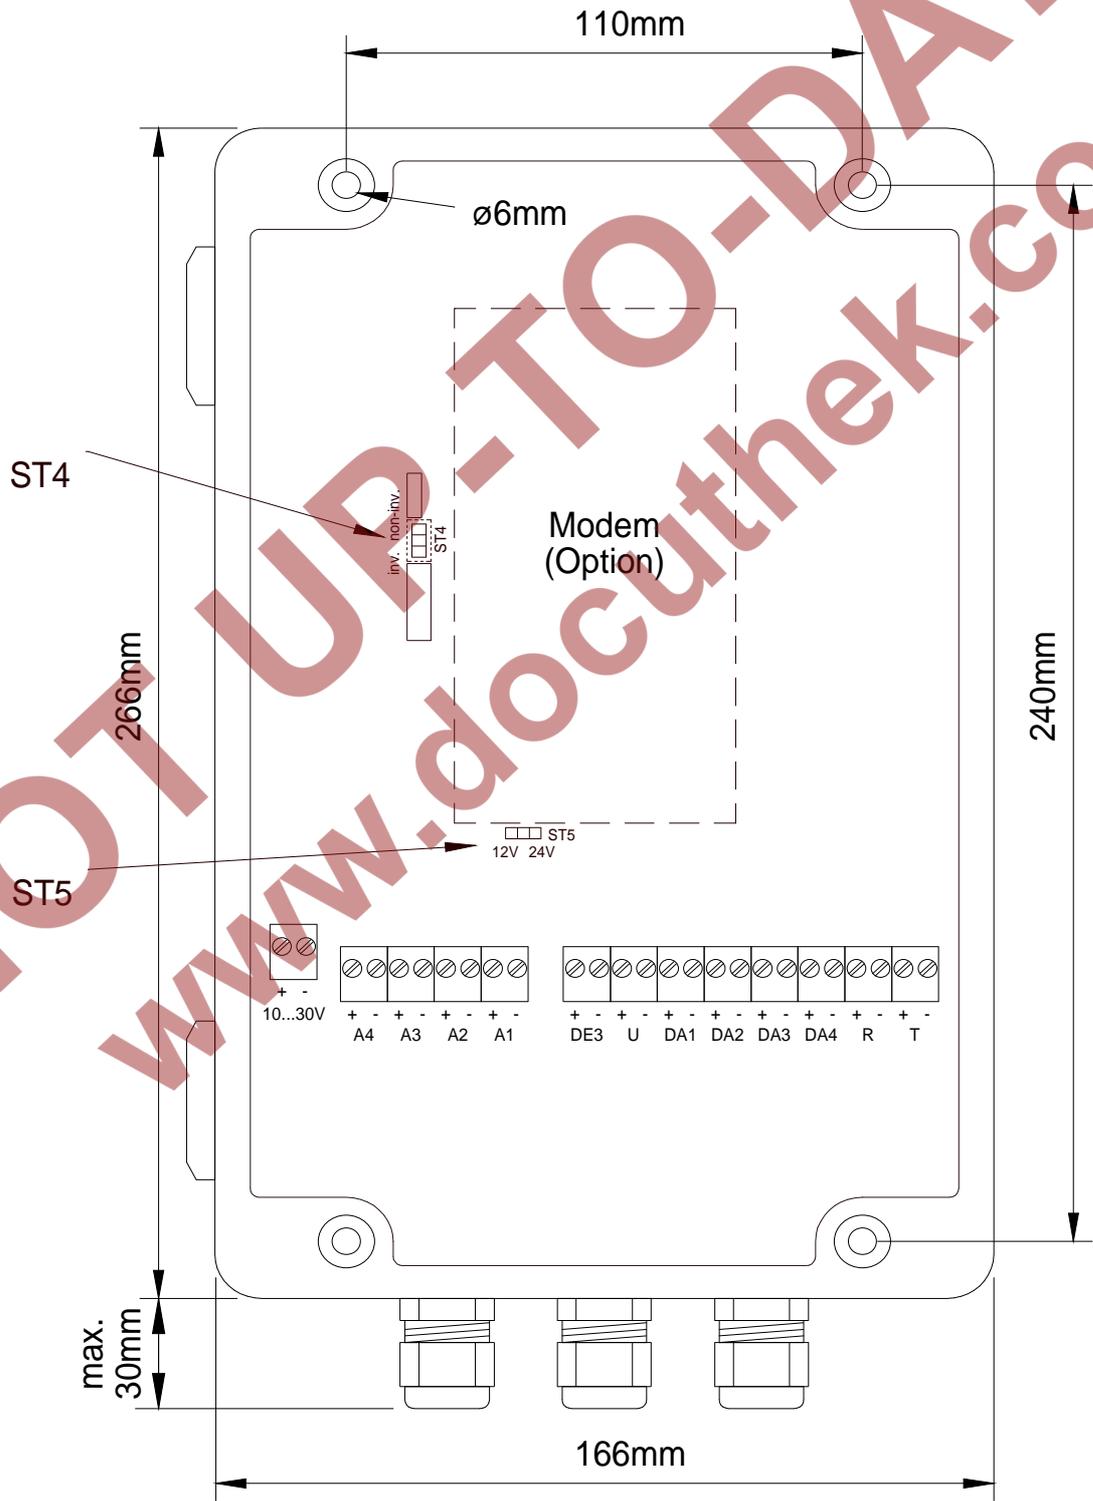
Sicht von oben auf das geöffnete Gerät (hier: „DC“-Ausführung)
